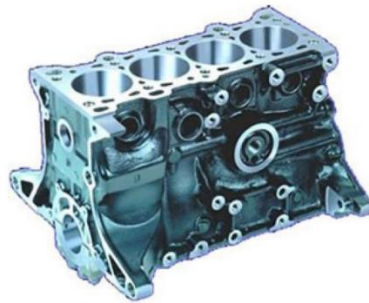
Bloque motor con camisas. Fuente: futurosmaquinistas [19]
